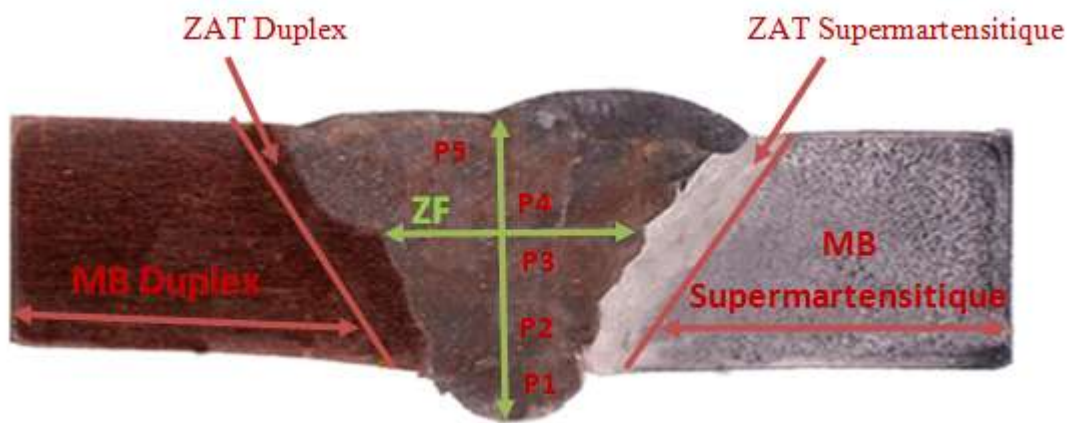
Macrographie du joint soudé avec ses zones principales.
